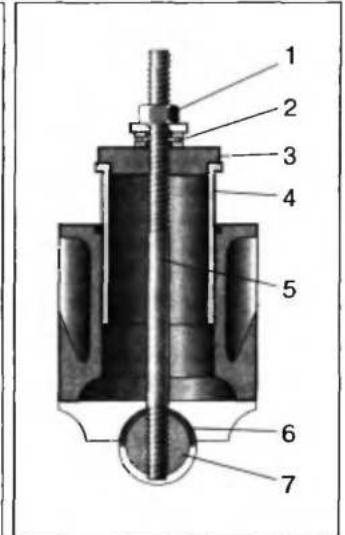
Винтовое приспособление для запрессовки "сухих" гильз:
